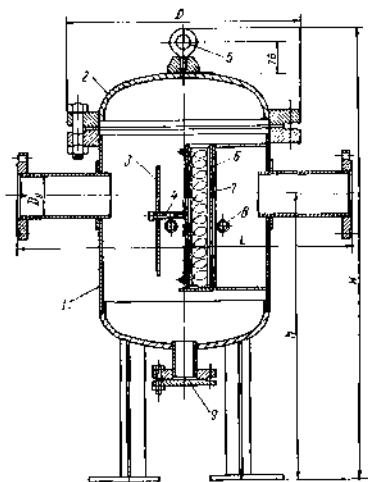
Фильтр кассетный сварной типа ФГ.
